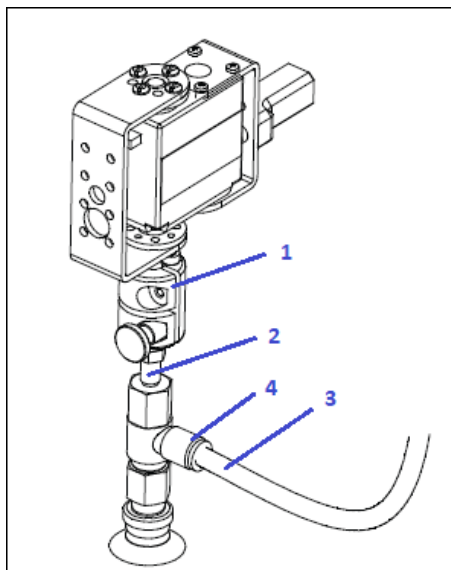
Поворотный модуль инструмента с присоской вакуумного захвата, где 1 – муфта поворотного модуля инструмента; 2 – хвостовик присоски; 3 – полиуретановая трубка для компрессора; 4 – фитинговый держатель
